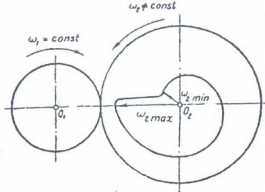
Цилиндрическая зубчатая передача с переменным делительным шагом
